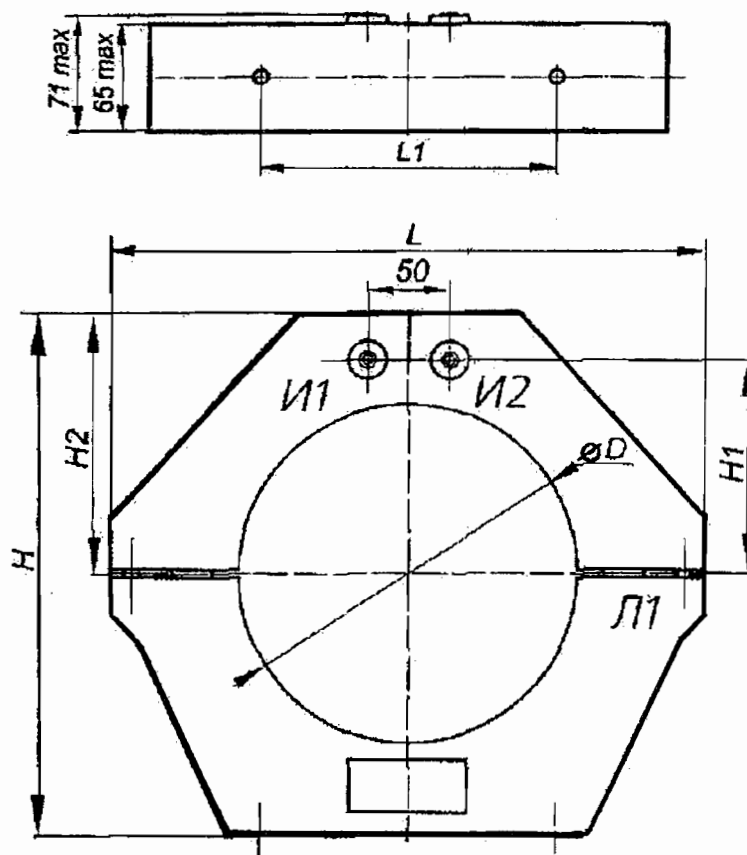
Общий вид и габаритные размеры трансформаторов тока типа ТЗЛКР
